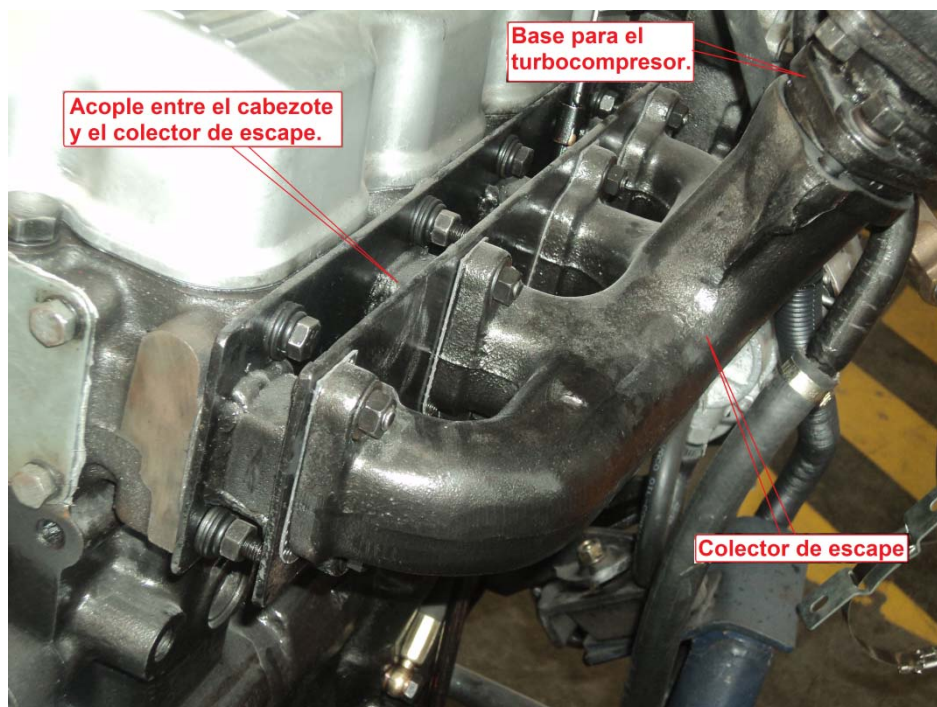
19 Montaje de acoples para el turbocompresor.
